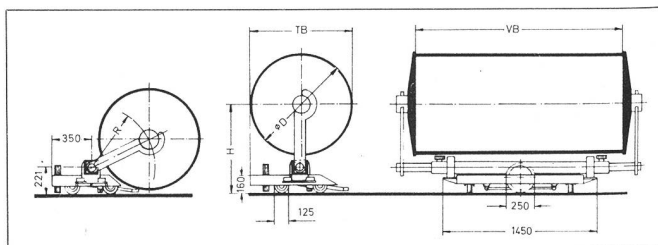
Platzsparend ausgelegter Universal-Schwenkhubwagen
